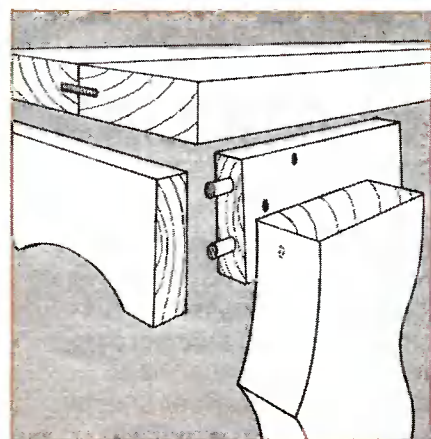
Ножки накладывают на элементы царги снаружи, а привинчивают шурупами изнутри. Предварительно контактирующие поверхности промазывают клеем.
